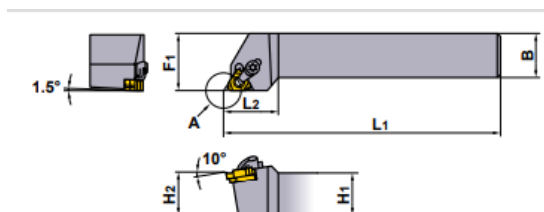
Державка MMTER2020K16-C [4 с. 445]
